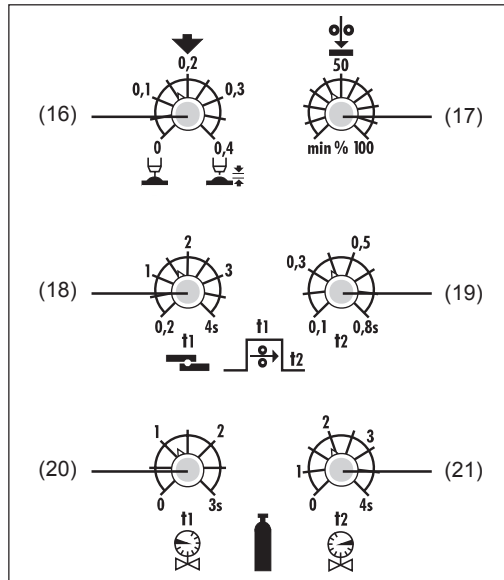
Divers régulateurs à la face interne de l'appareil de soudage
